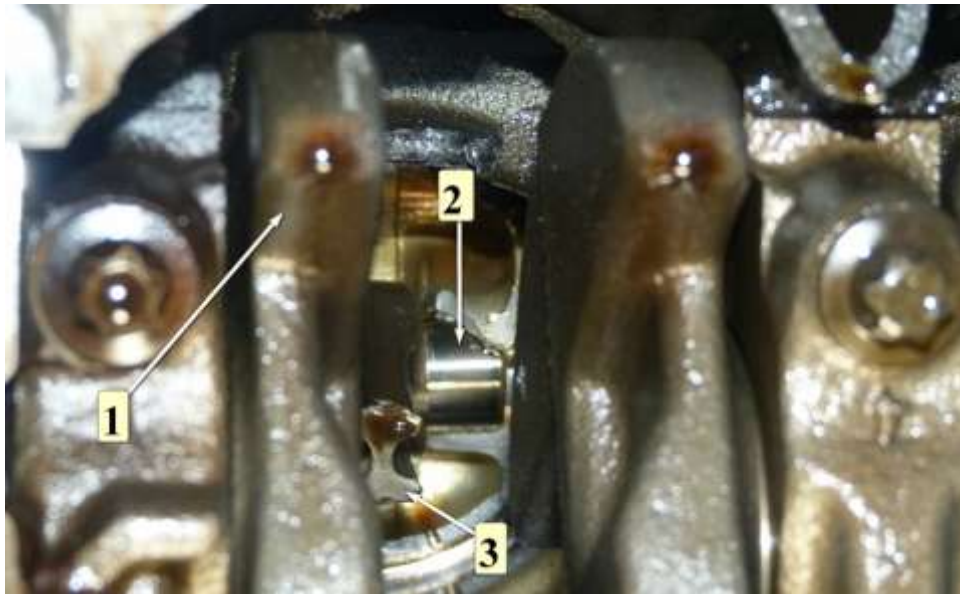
Вид снизу на поршень, поршневой палец и верхнюю часть шатуна 4-го цилиндра: 1 – коленчатый вал; 2 – поршневой палец; 3 – верхняя часть шатуна
